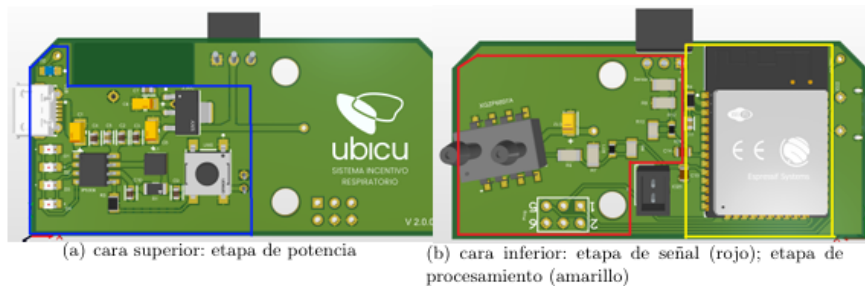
PCB del sistema Ubicu(Fuente:[8])
